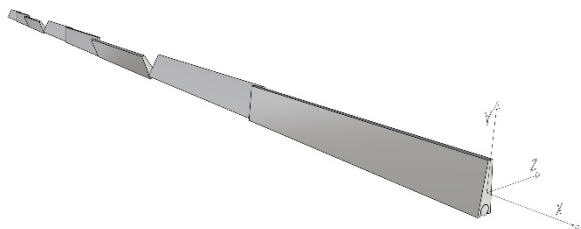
Ejemplo modelo estructural vista 3D y sistema de coordenadas del elemento analizado de la categoría 5.5 m (caso “patrón”).
